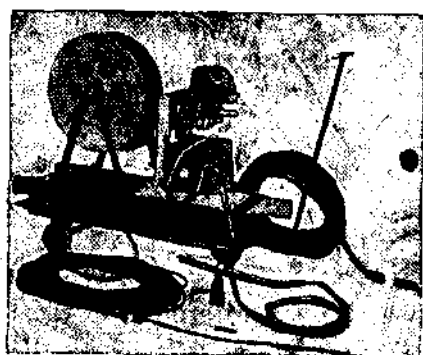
Передвижной сварочный полуавтомат.
